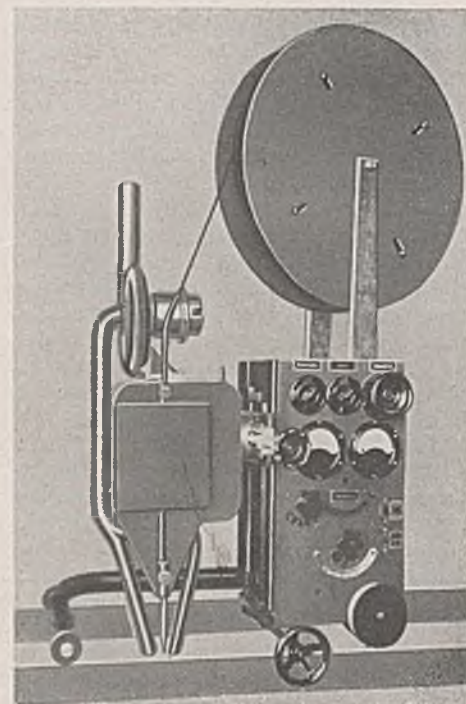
Selbsttätige Schweißeinrichtung mit Schweißkopf für blanken Draht.
